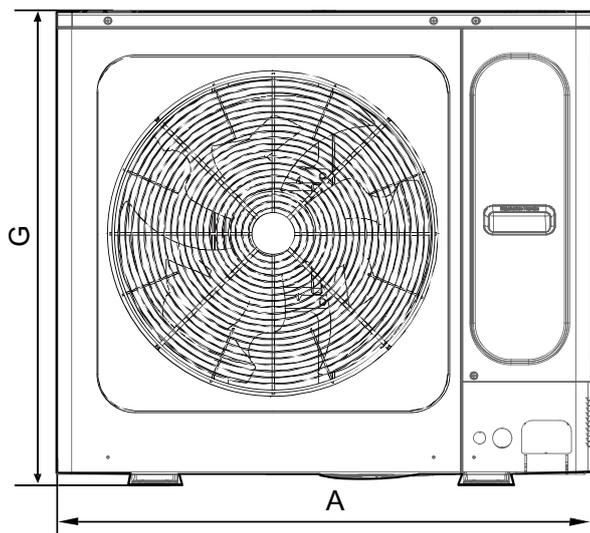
modèles 120 à 160 Dimensions en vue de face (unité : mm)
